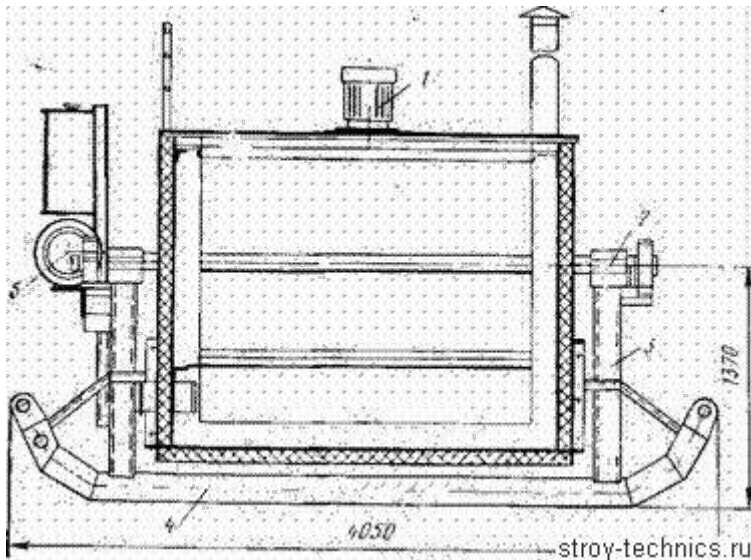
Котел для варки битума УБВ-1 с поворотным устройством
